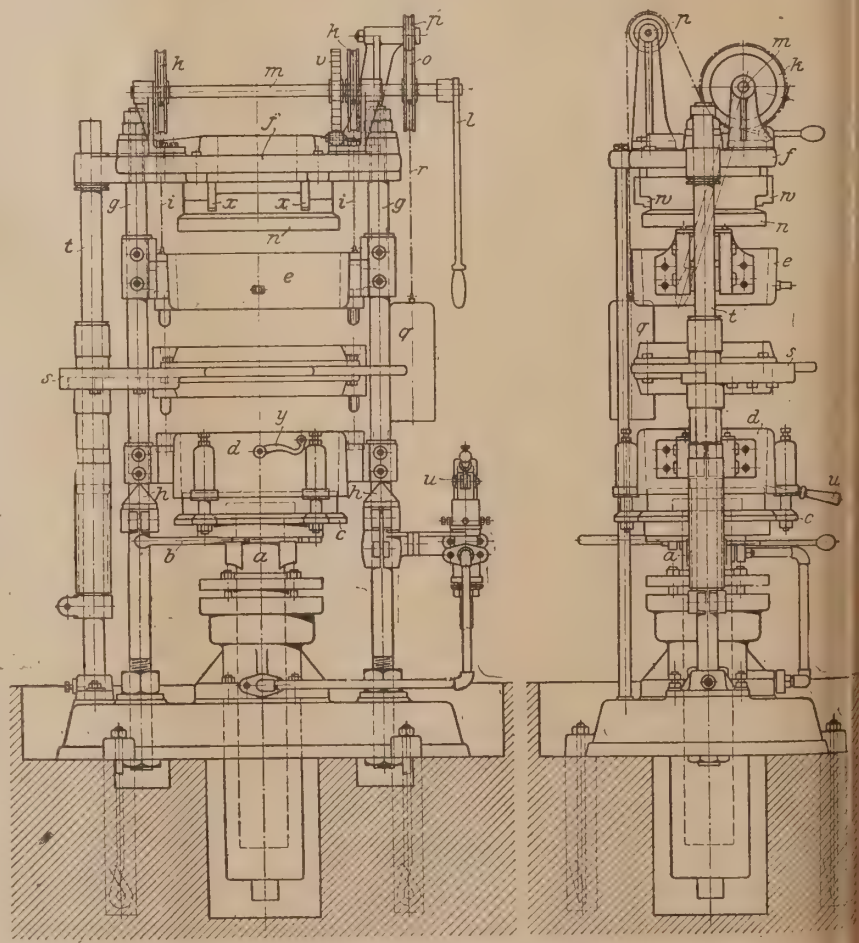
und 6. Hydraulische Formmaschine für kastenlose Formen.
